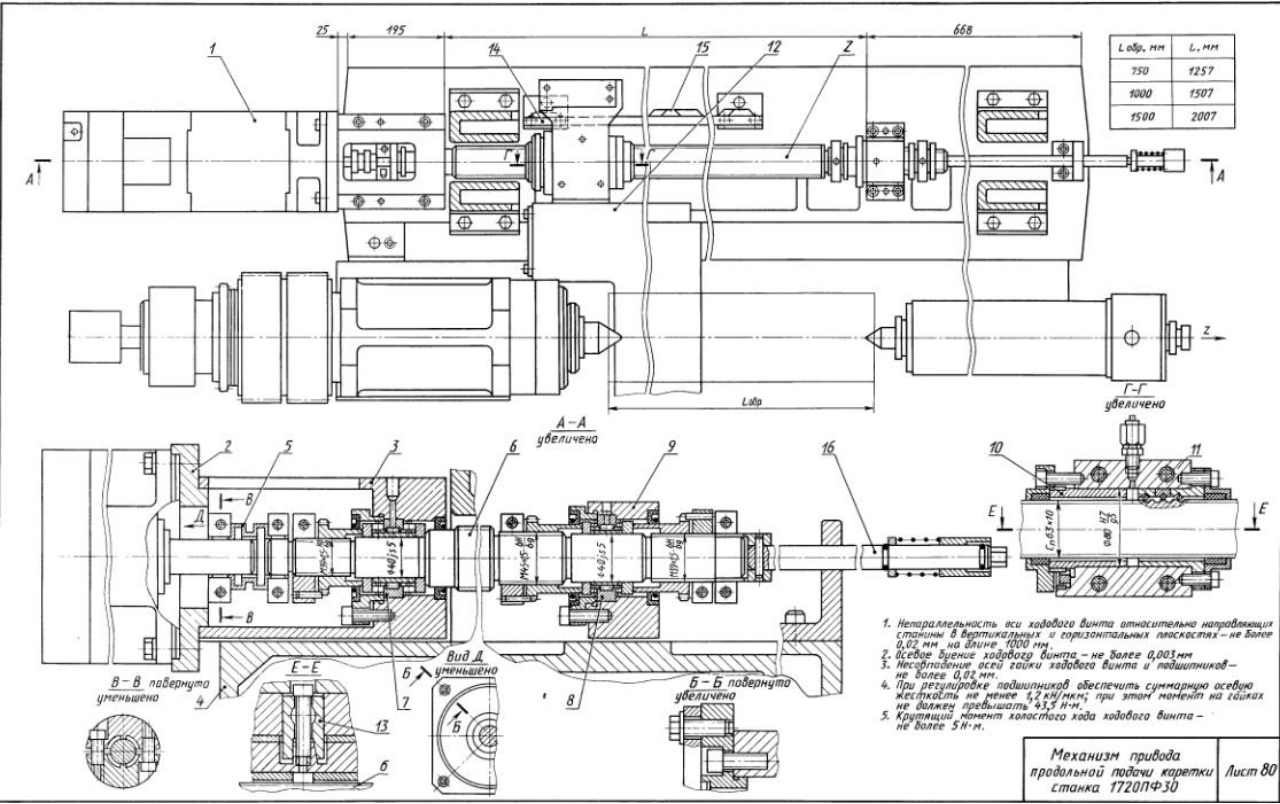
Механізм приводу поздовжньої подачі каретки верстата.
